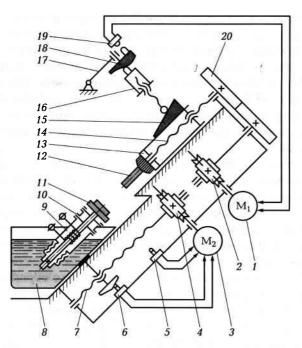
Электроискровая установка для обработки деталей методом копирования электрода-инструмента:
